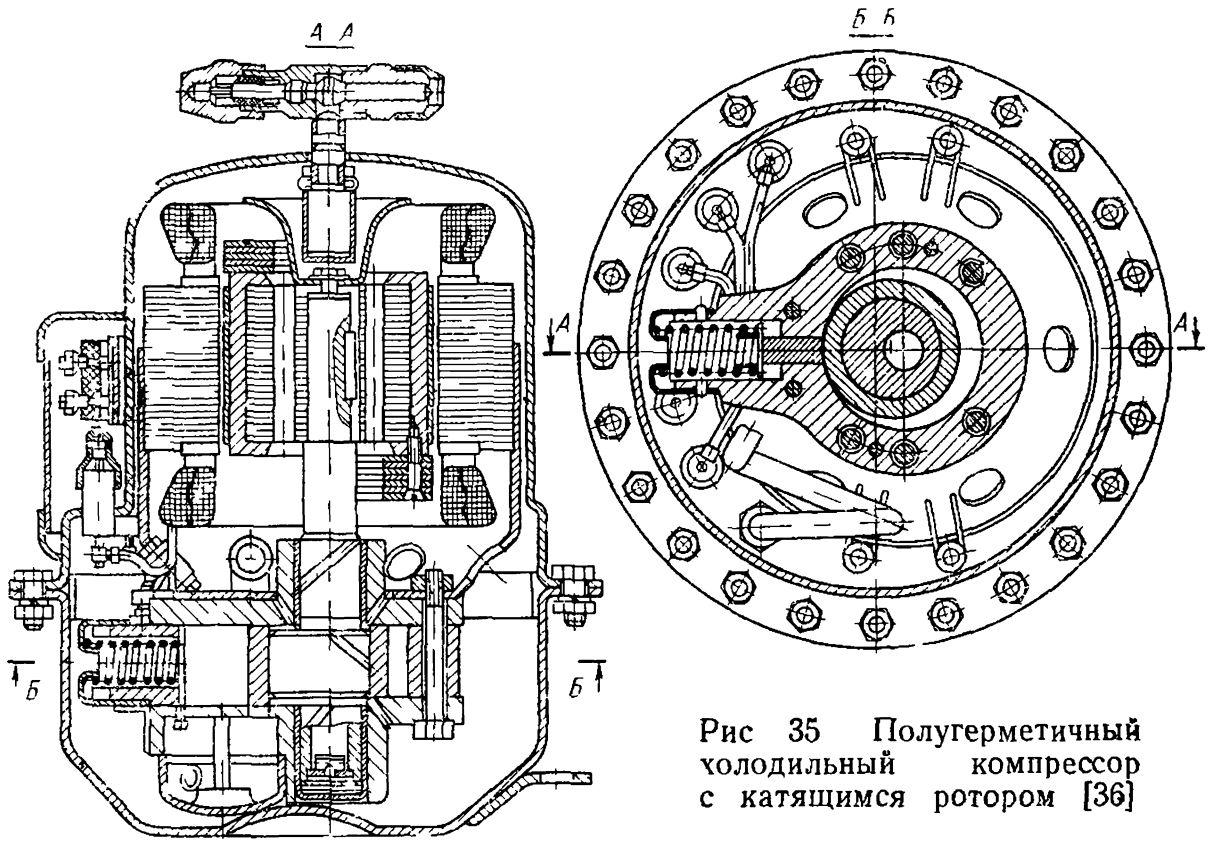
Полугерметичный холодильный компрессор с катящимся ротором [36]
